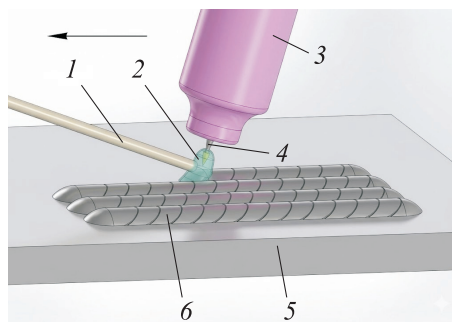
Схема дуговой наплавки неплавящимся электродом в среде инертных газов рабочего слоя многослойной композиции (стрелкой указано направление наплавки)
